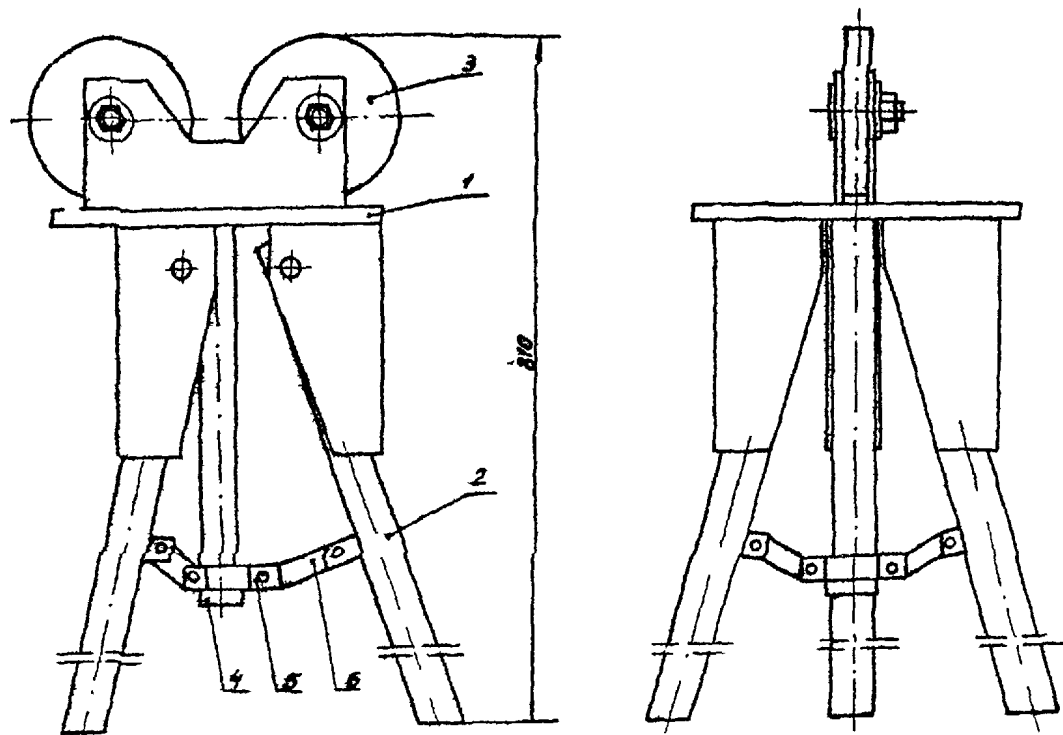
Подставка для укладки деталей тормозной системы: 1 - основание; 2 - ножка;
